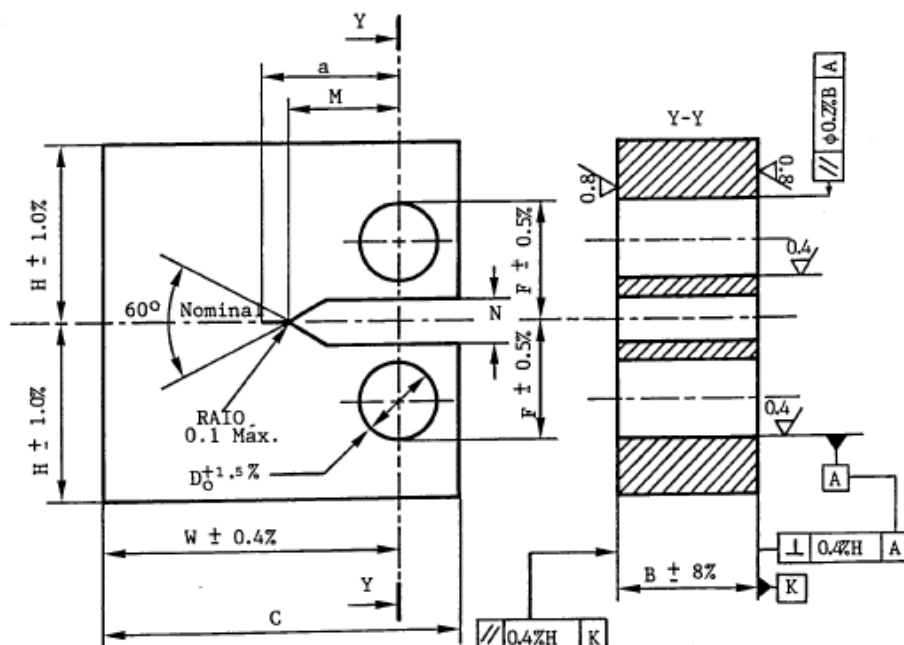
Desenho Técnico do Provete CT.
